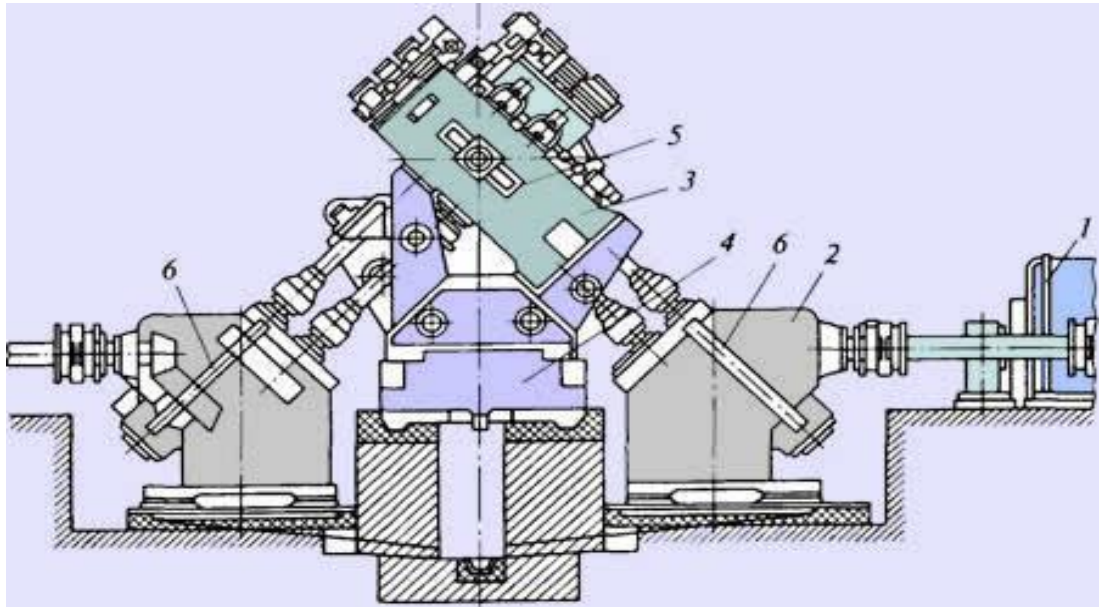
Безперервний дев'ятиклітьовий стан з приводом через конічний редуктор (поперечний розріз):
